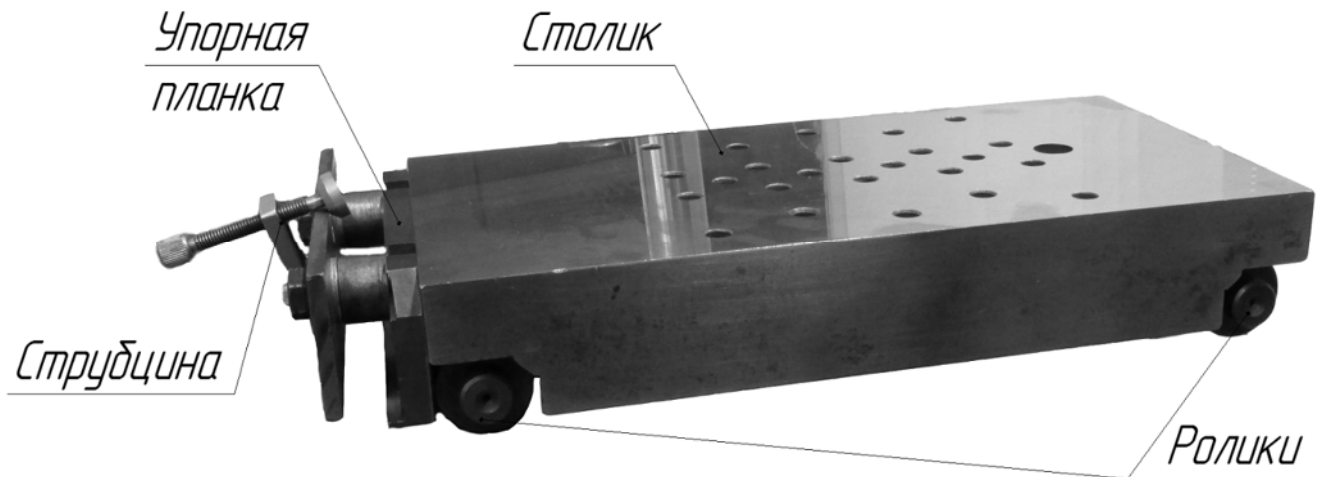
Конструкция синусной линейки для измерений калибров с фланцем
